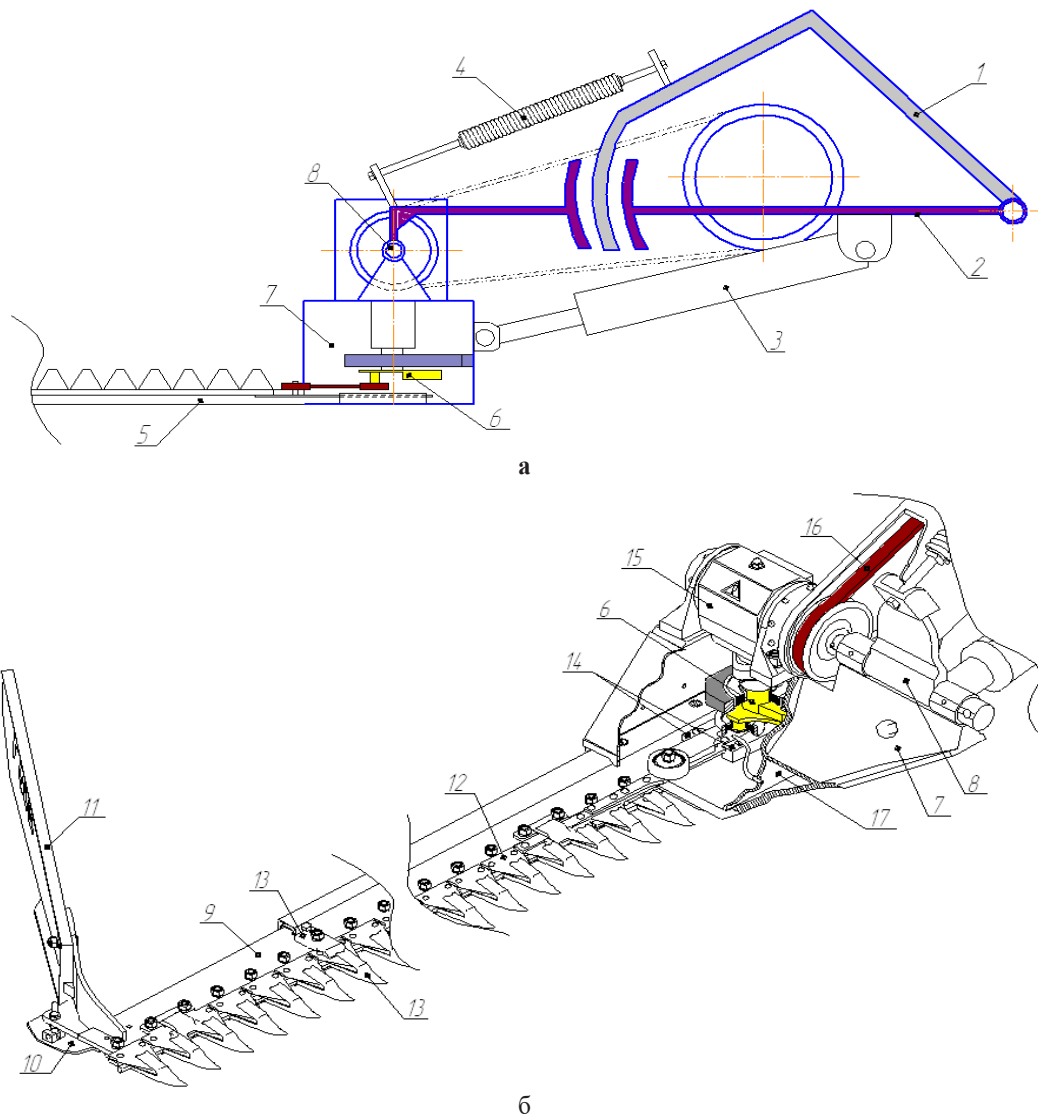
Общая схема устройства (а) и 3D-модель режущего аппарата косилки с аксиальным расположением кривошипно-шатунного механизма (б):
